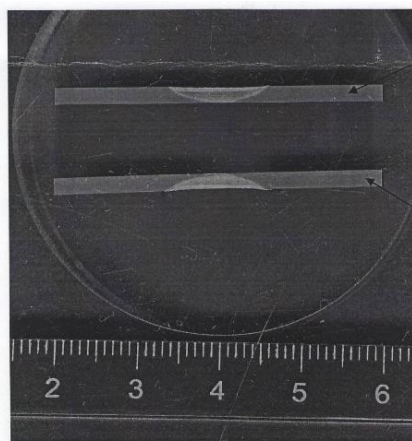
Образцы для металлографического исследования сварного шва титанового сплава ВТ-6
